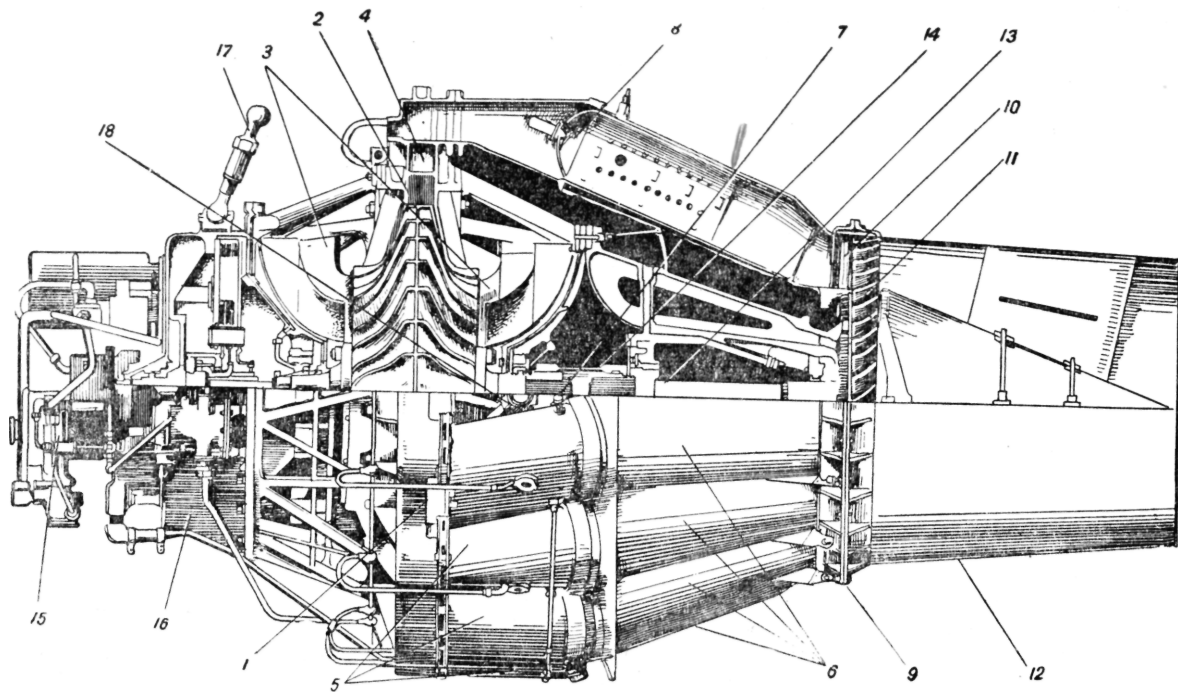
Турбореактивный двигатель с центробежным компрессором:
